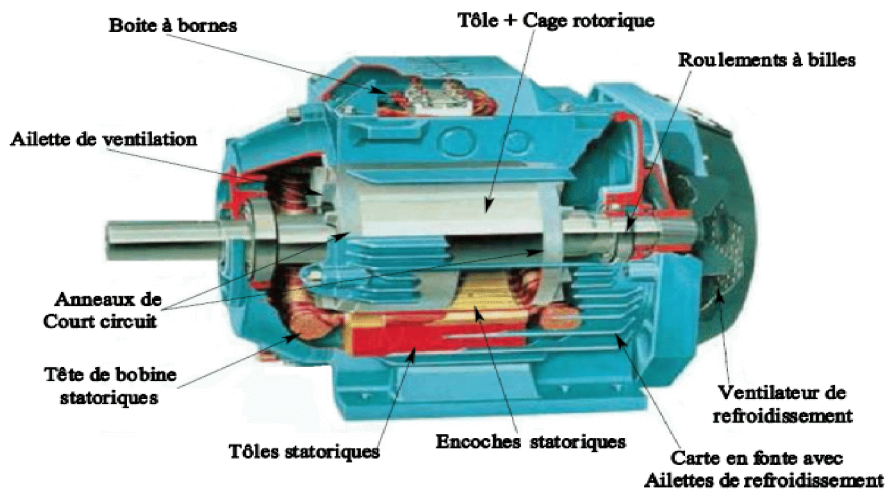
Vue d'ensemble d'une machine asynchrone à simple cage d'écureuil.
